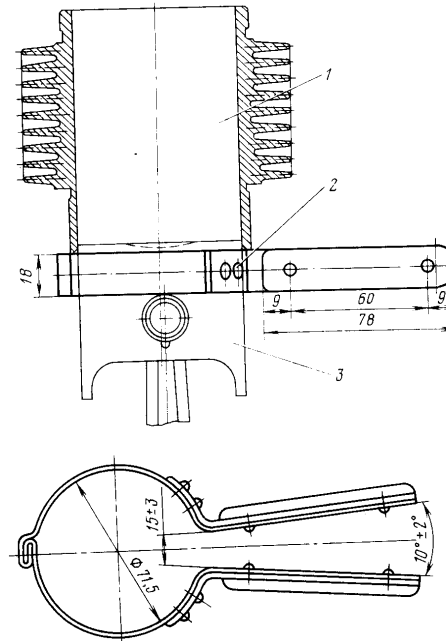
Приспособление для обжима поршневых колец: 1 - цилиндр; 2 - приспособление; 3 - поршень с кольцами
